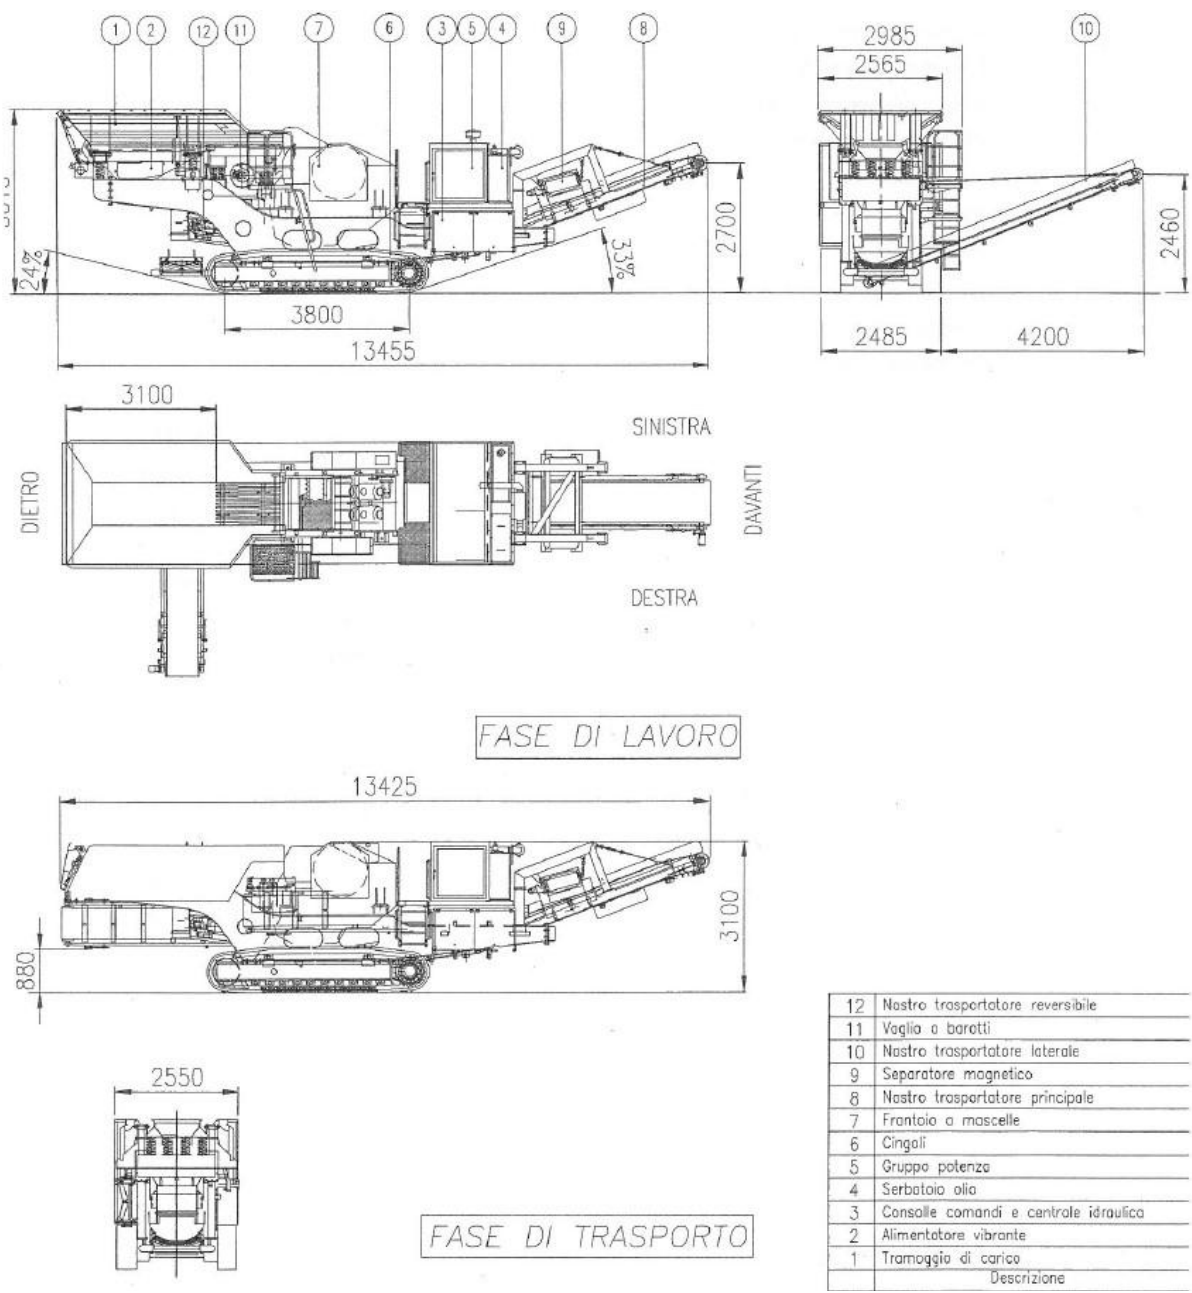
schema dell'impianto di frantumazione e dei suoi componenti.
